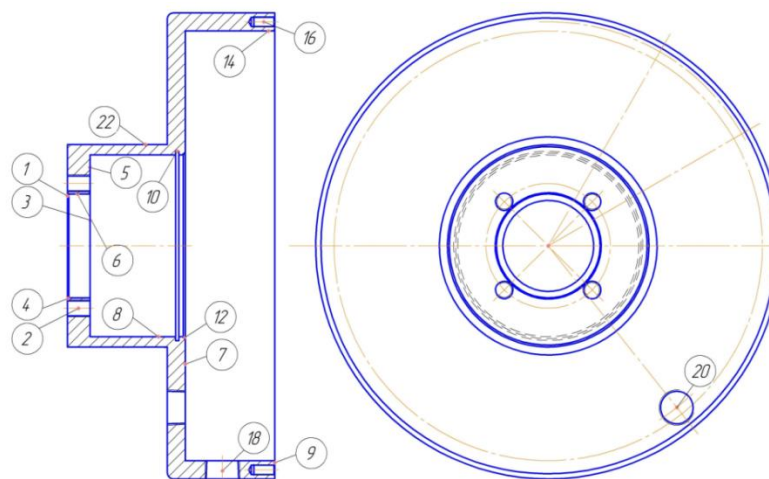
Нумерация обрабатываемых поверхностей детали
